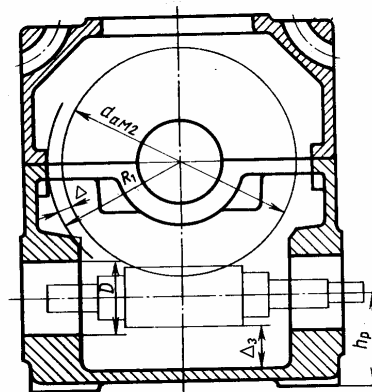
Корпус с разъемом в плоскости оси вала колеса червячного редуктора
